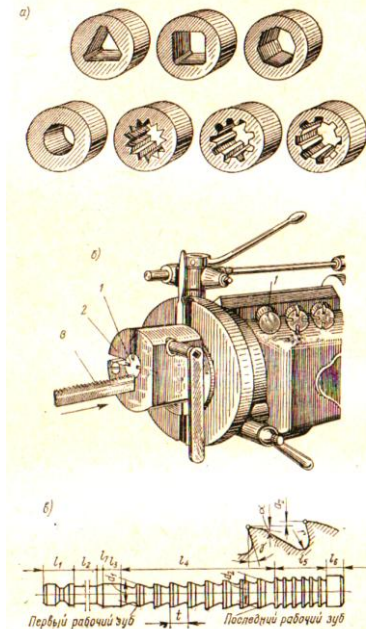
Протягивание деталей: а-формы поверхностей, обрабатываемых внутренним протягиванием; б – протягивание пазов шпоночной протяжкой; в – элементы и геометрические параметры режущей части круглой протяжки(в мм):
